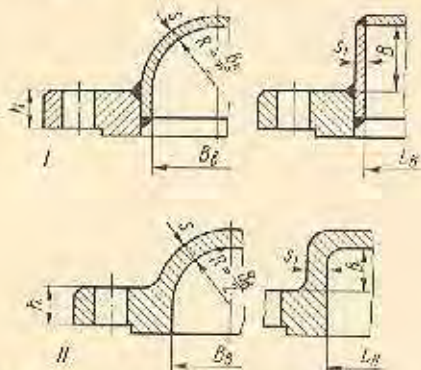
Основные типовые конструкции фланцевых цилиндрических крышек: I — сварные; II — литые
